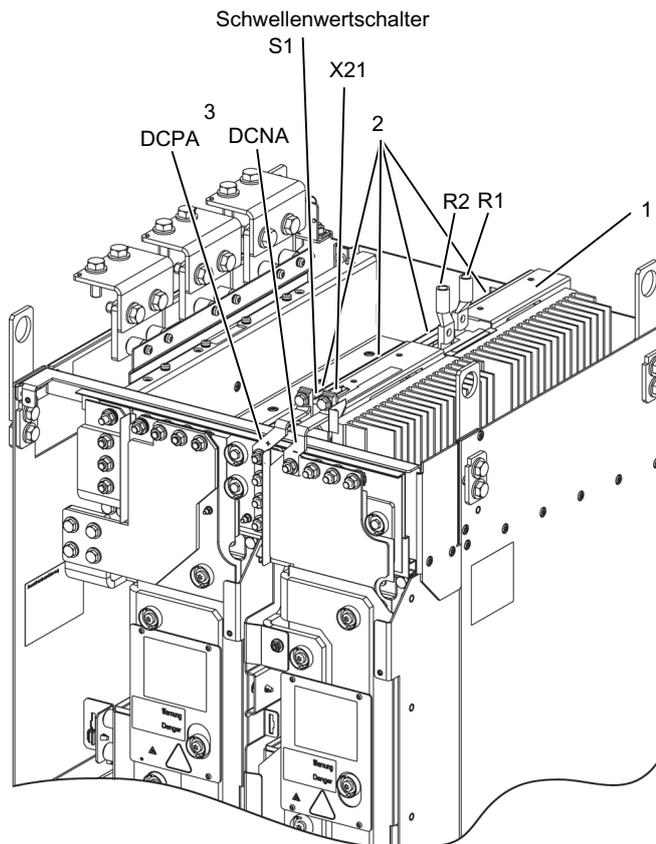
Montage des Braking Module in ein Power Module Bauform HX
